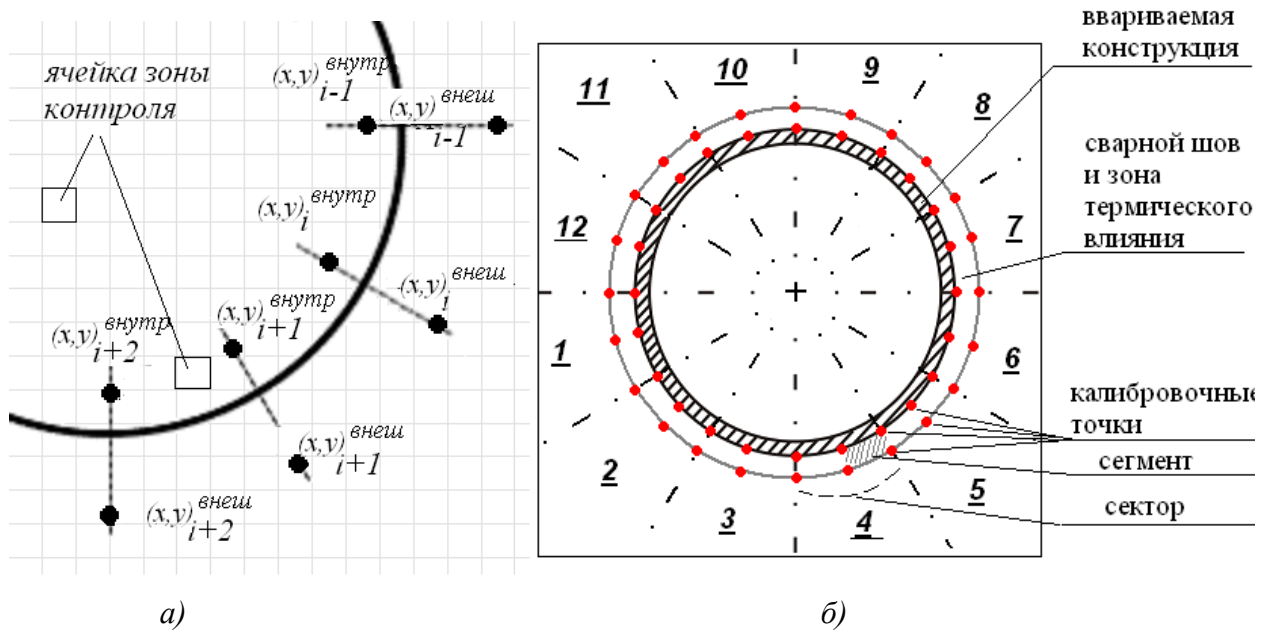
Разбиение кольцевого контура сварного шва на расчетные сегменты (а);
